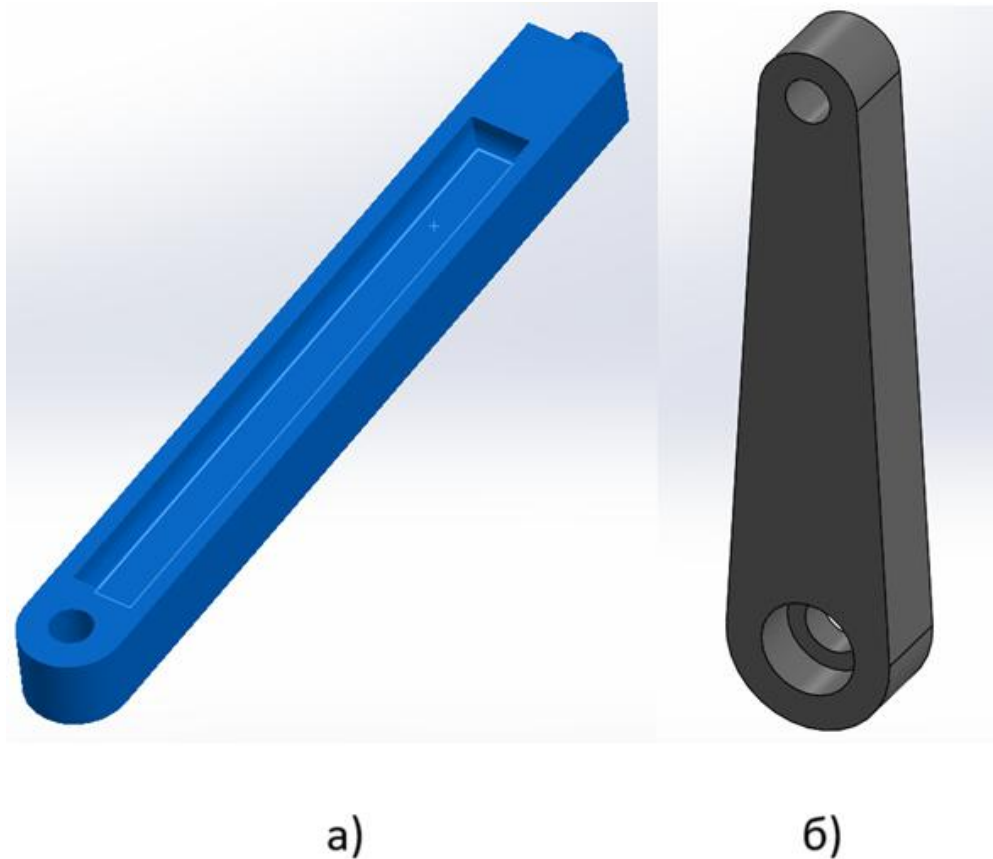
Елементи кінематичного ланцюга: а) сполучна штанга; б) важіль сервопривода
